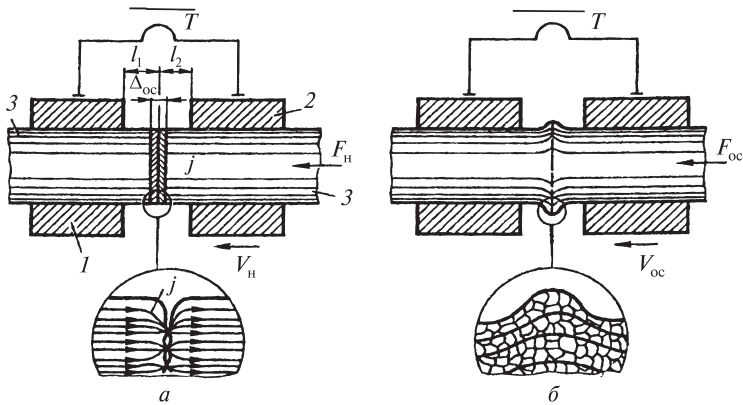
Схема стыковой сварки сопротивлением:
